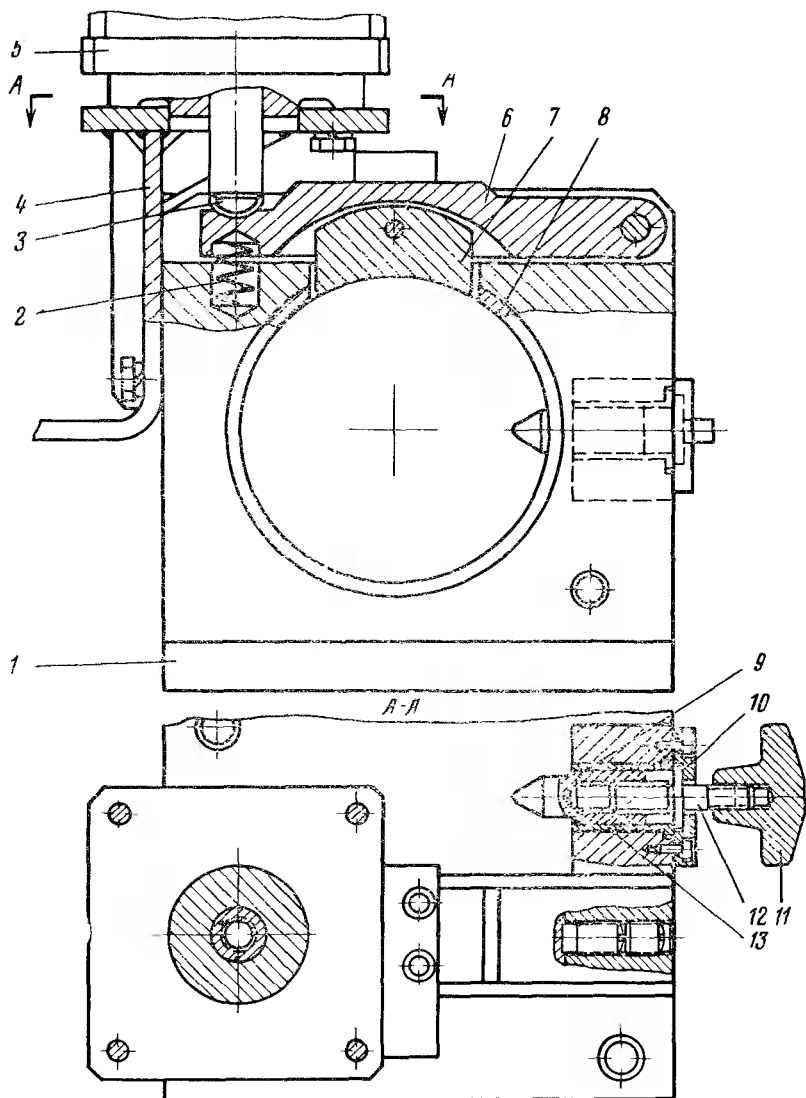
Приспособление для сборки и разборки вала ведущей шестерни заднего моста:
